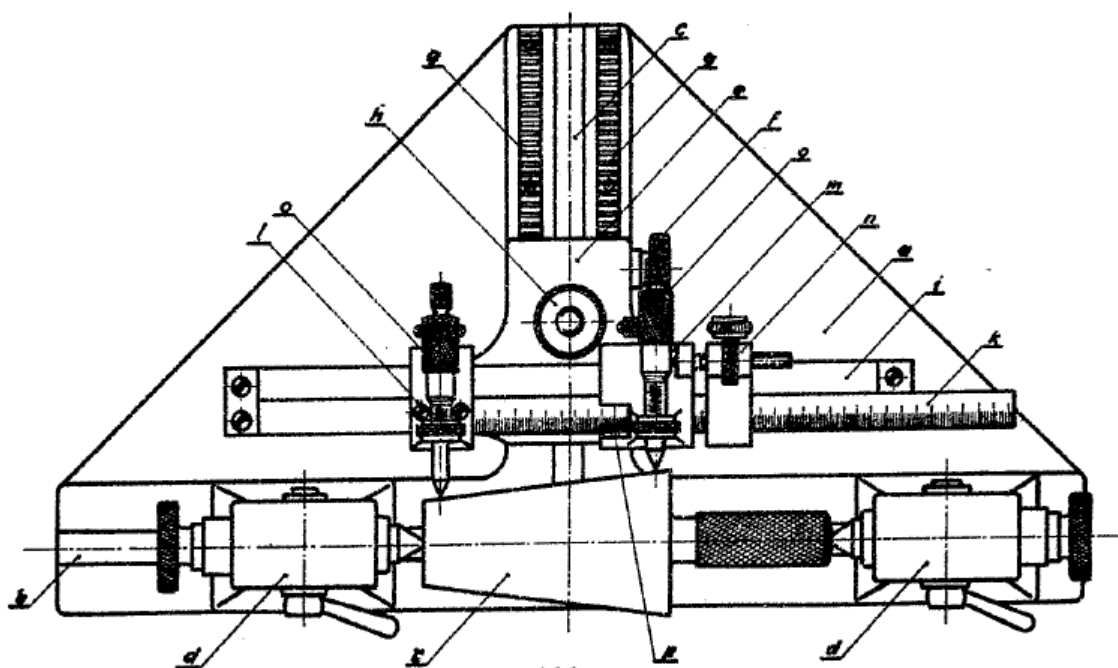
Пристрій для вимірювання калібру- пробки
